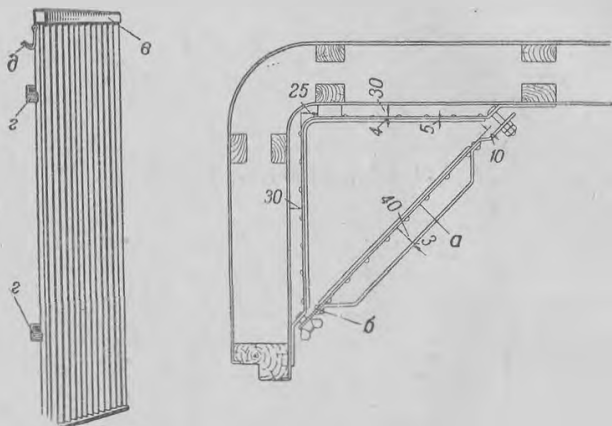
Охлаждающий прибор (бачок) и площадка для установки приборов:
